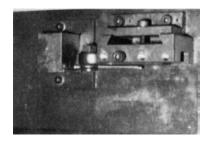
Контурное фрезерование и промежуточное приспособление
